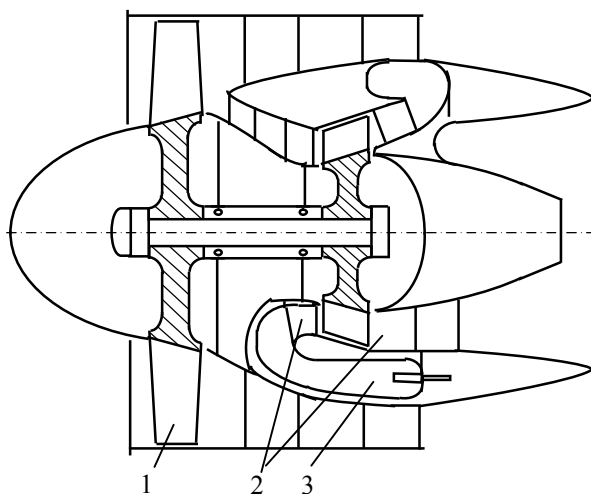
Схема газотурбинного двигателя с ТКО: 1 – вентилятор; 2 – турбокомпрессор (ТКО); 3 – камера сгорания
